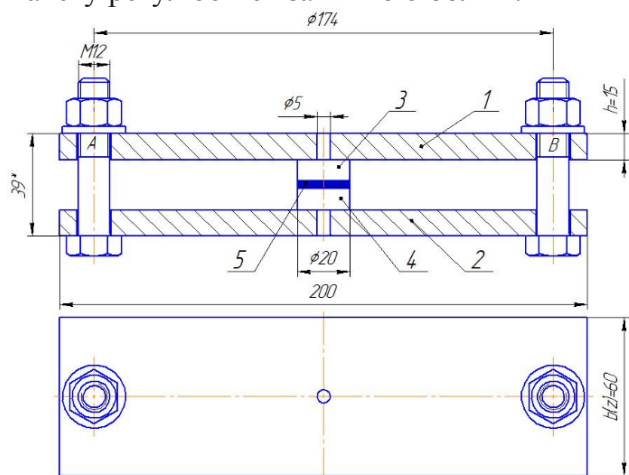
Установка для зварювання тиском: 1. – плита верхня; 2. – плита нижня; 3,4 – притискачі; 5 – пакет.
